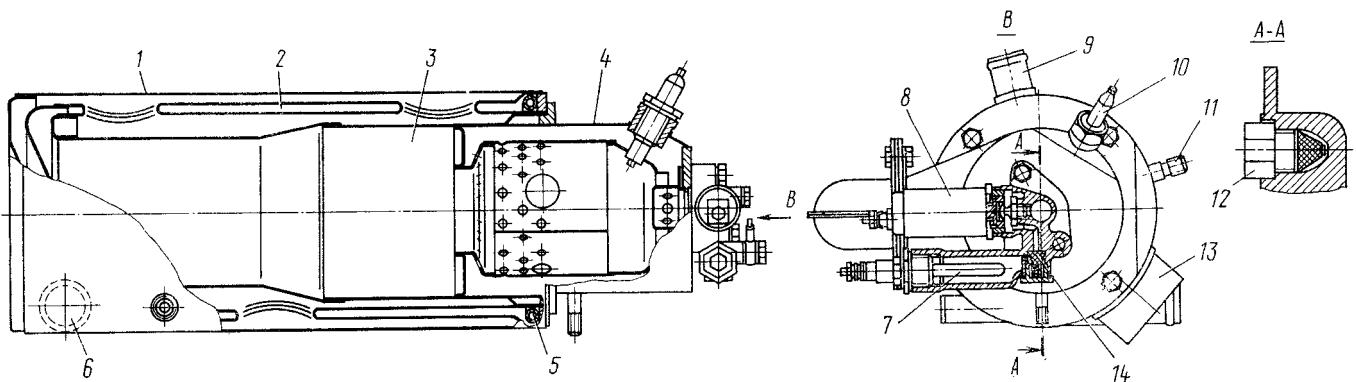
Теплообменник подогревателя: 1 - теплообменник; 2 - газоход обратный; 3 - газоход прямой; 4 - горелка; 5 - нагреватель газового топлива; 6 - патрубок подвода жидкости; 7 - электронагреватель топлива; 8 - клапан электромагнитный; 9 - патрубок отвода жидкости из теплообменника; 10 - свеча электроискровая; 11 - штуцер подвода топлива к нагревателю в теплообменнике; 12 - форсунка; 13 - патрубок отвода отработавших газов; 14 - фильтр топливный
